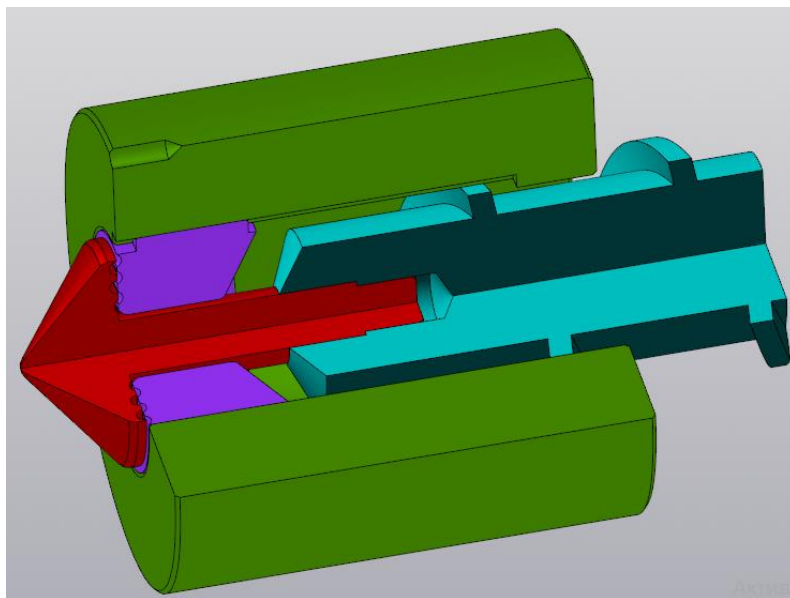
Готова збірка модернізованого вузла
